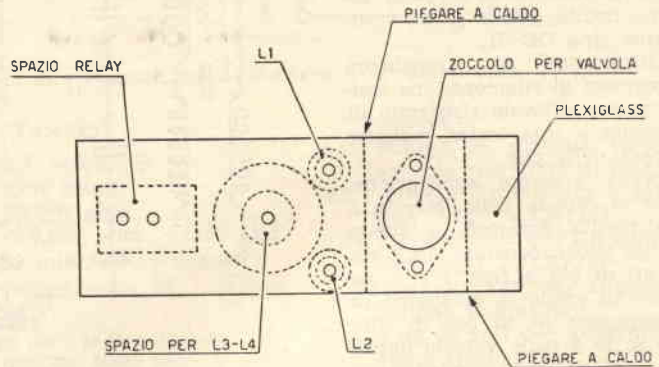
Disposizione in pianta dei componenti su telaio in plexiglas
